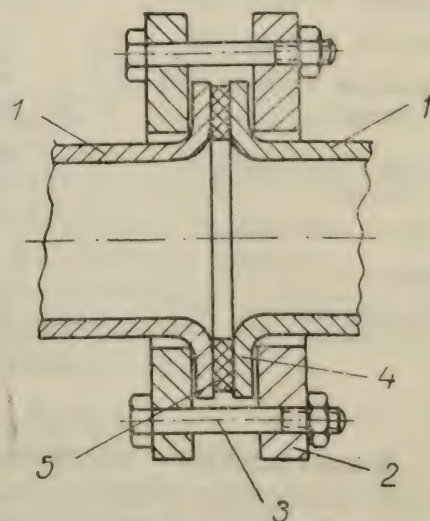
Крепление труб на фланцах при помощи отбортовки:
